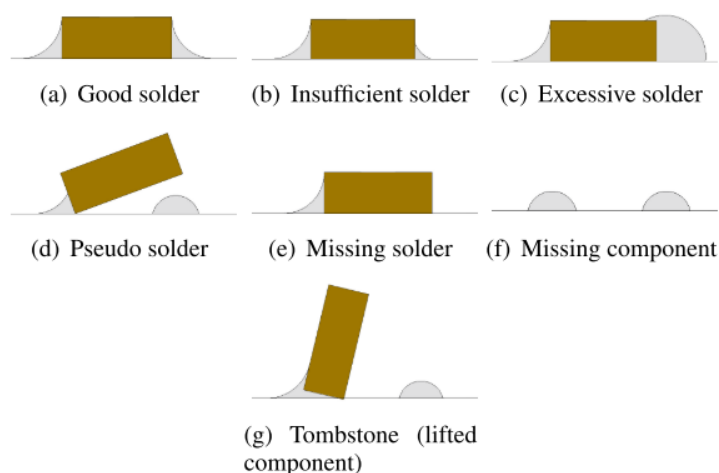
Defectos comunes de soldadura, tomado de [2]
